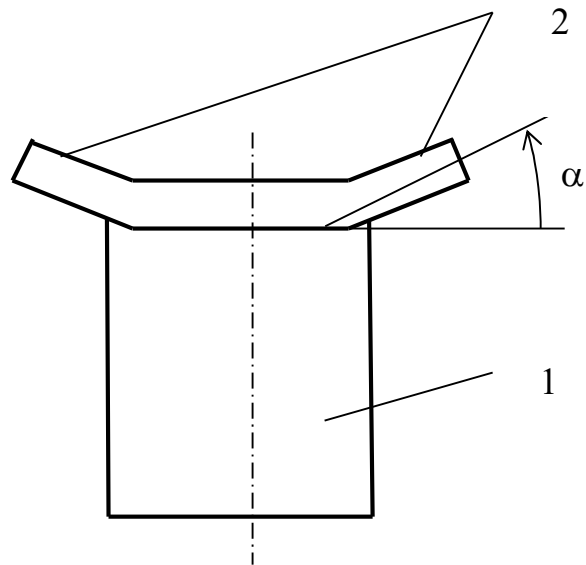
Фронтальний вигляд пожежного монітора: 1 – корпус; 2 – насадки
